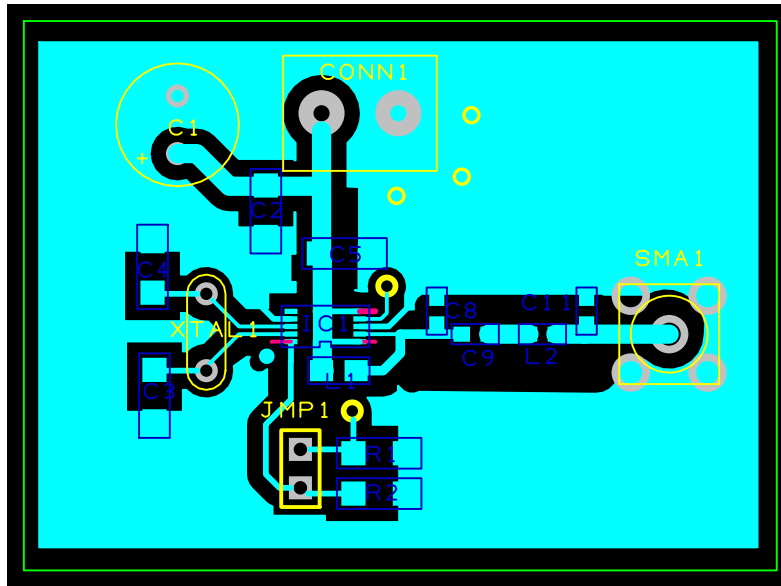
PCB del modulo trasmettitore: è visibile il lato rame e l'ingombro dei componenti
